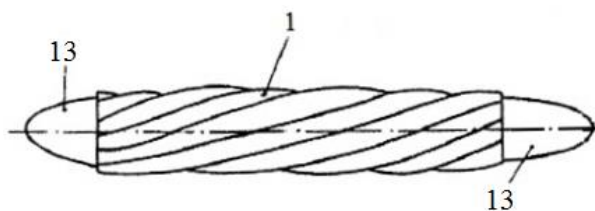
Транспортная машина для перемещения под водой с винтовым движителем предлагаемой конструкции (общий вид)
